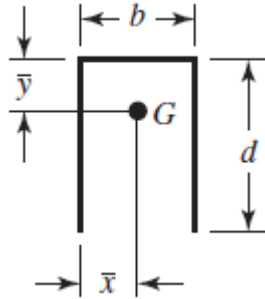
Patrón de soldadura para la unión de la viga a las columnas
